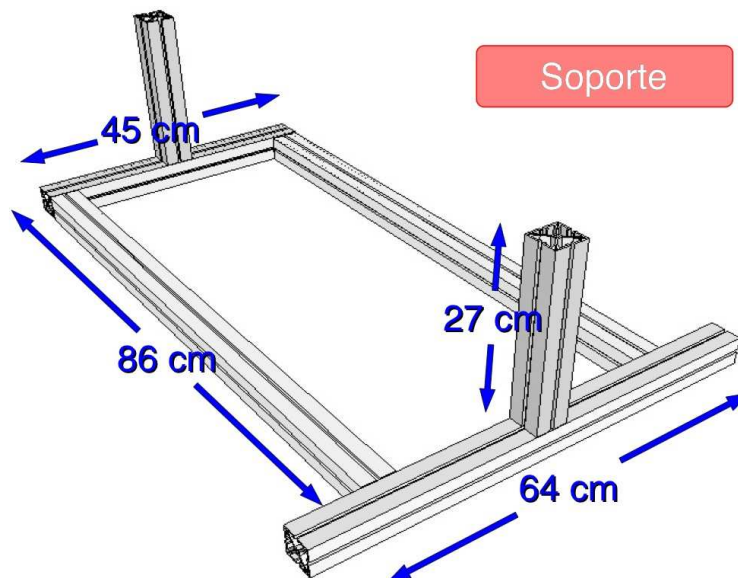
Cotas del soporte de aluminio de la bicicleta.
